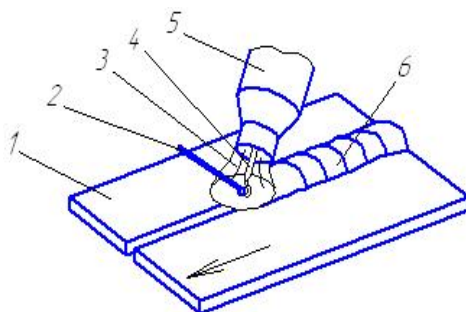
Схема аргонодуговой сварки: 1 – свариваемое изделие; 2 – присадка; 3 – защитный газ; 4 – вольфрамовый электрод; 5 – сопло горелки; 6 – шов
